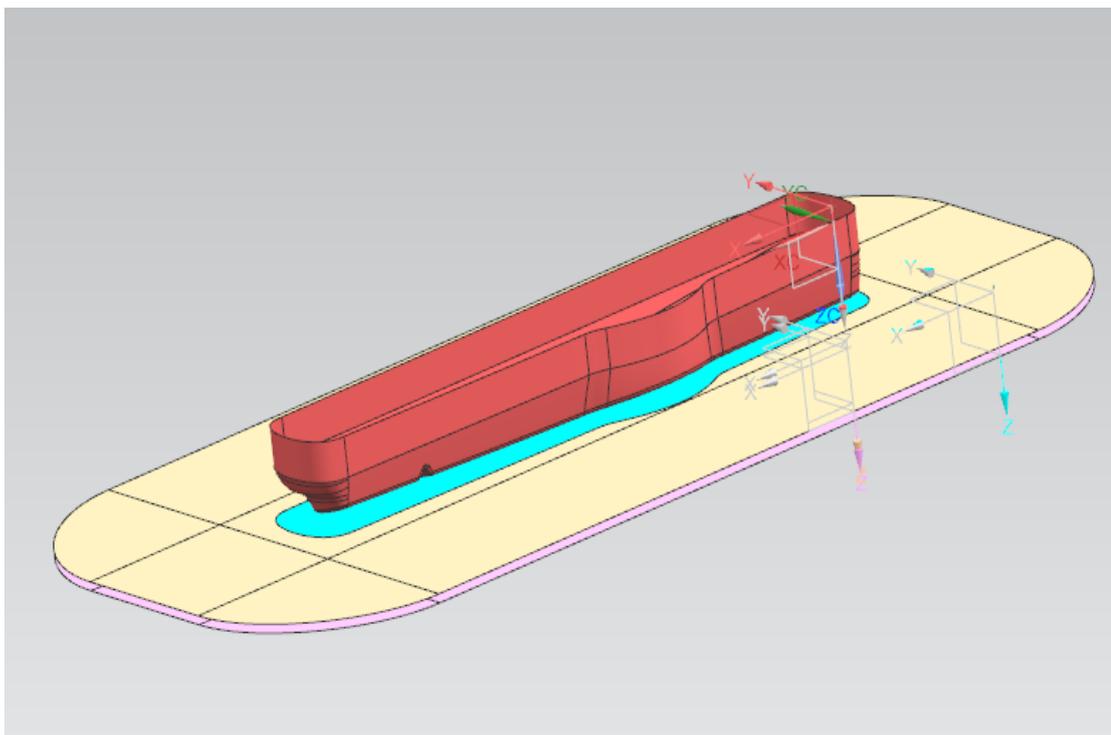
Ассоциативные копии всех поверхностей заготовки и рабочего инструмента
